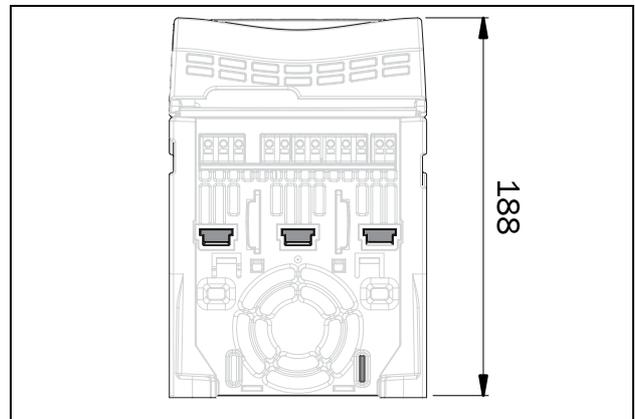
Dimensions des formats de châssis 1 et 2 du TSA, vue du dessous
